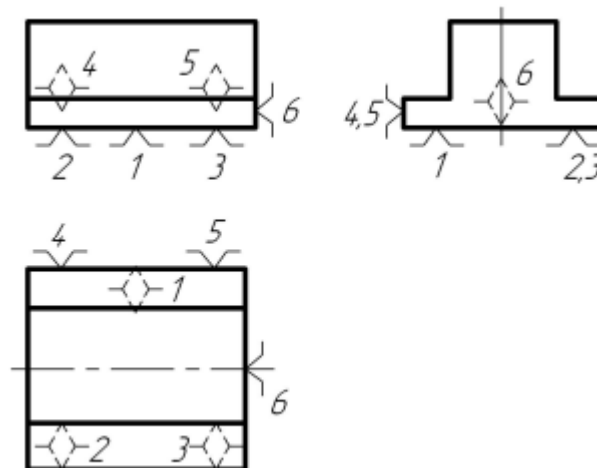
Установлення заготовки на площину основи і дві бокові сторони
